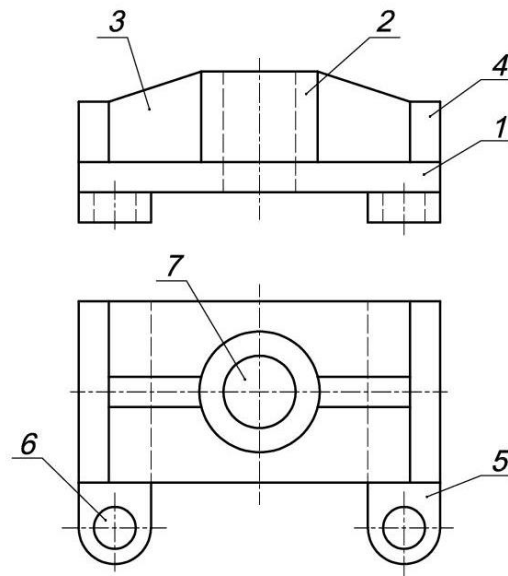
Розбивка деталі на формоутворюючі геометричні фігури
